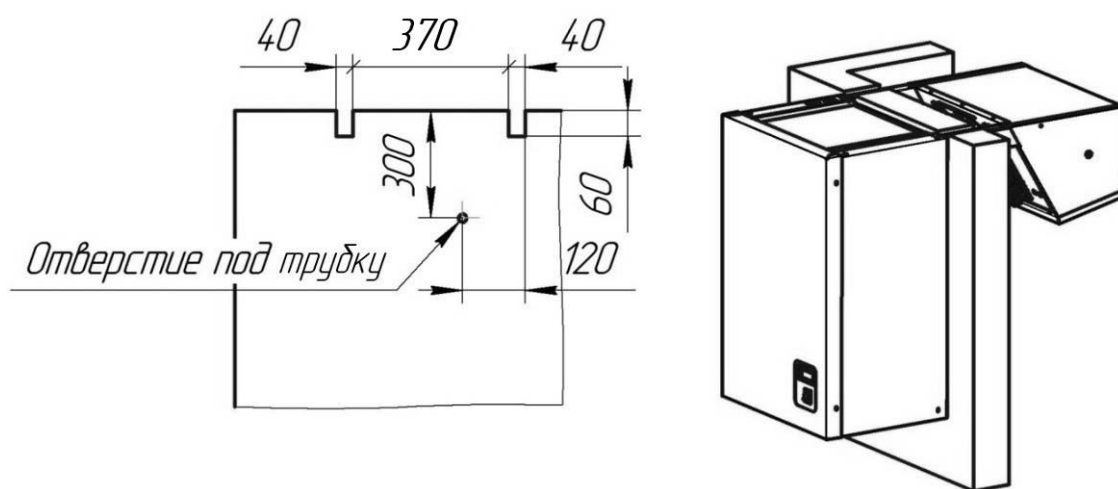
1. Доработка стенки камеры для установки моноблока
